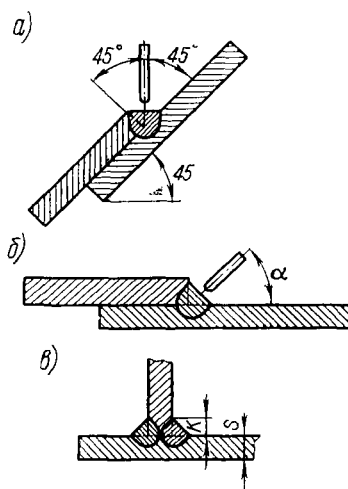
Угловые швы при сварке под флюсом:
